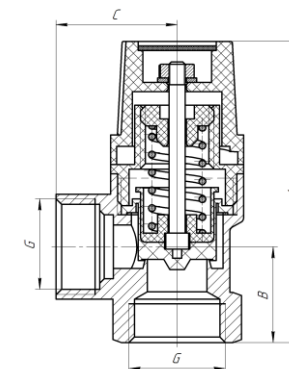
Габаритные и присоединительные размеры изделия.
